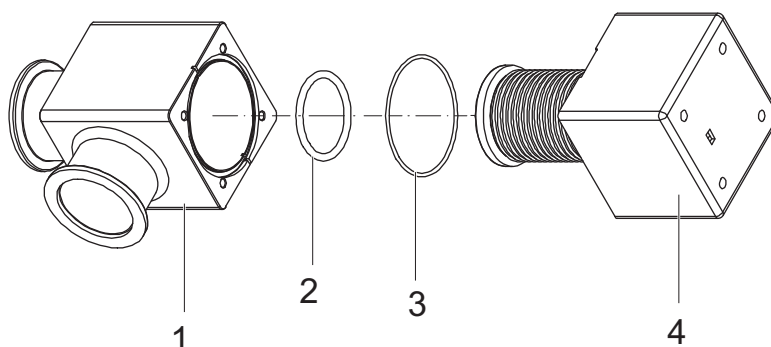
Entnehmen und Reinigen der O-Ringe, elektropneumatisches Eckventil
